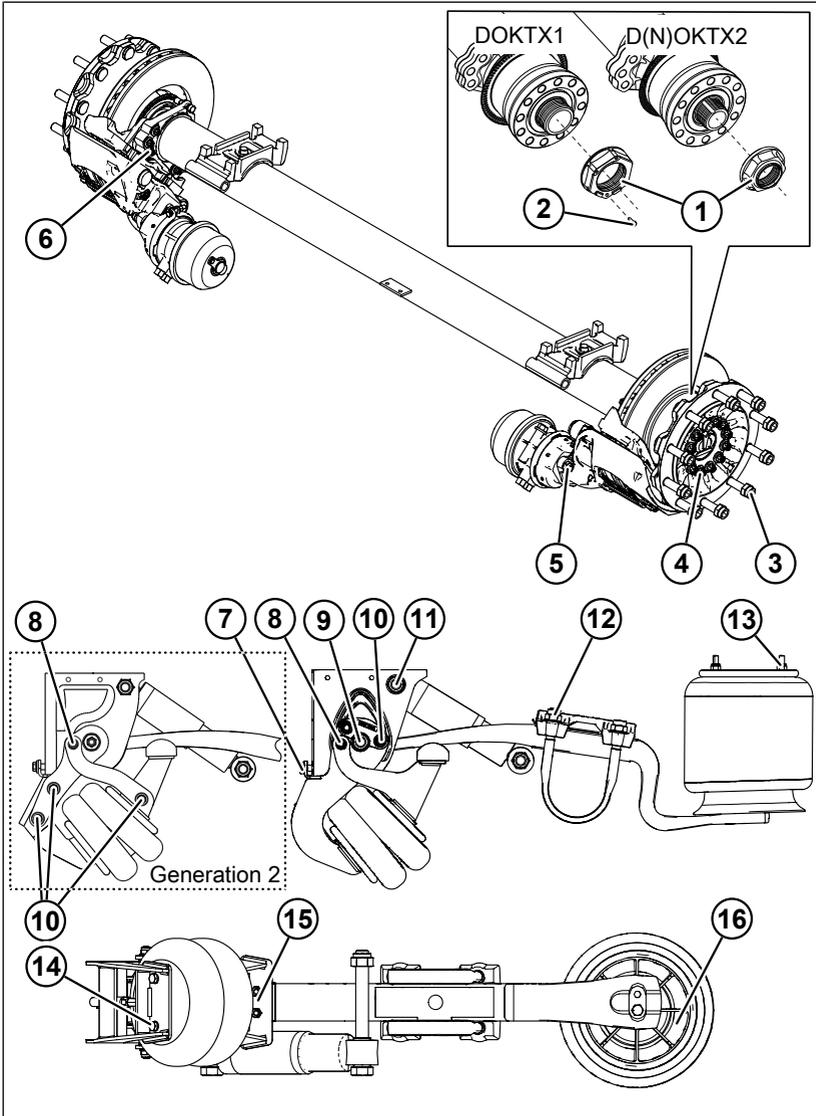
Vue d'ensemble des couples de contrôle et de serrage (bras de suspension pneumatique supérieur)
